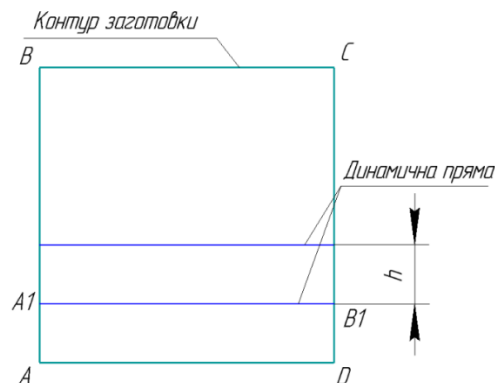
Схема контуру заготовки з динамічними прямими
